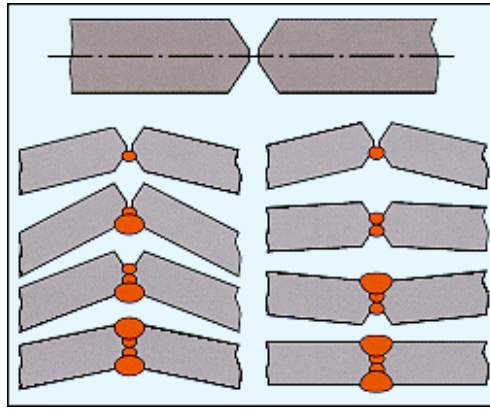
Figura 1 - Junta de topo - chanfro simétrico com múltiplos passes. (a) Sequência de soldagem realizada de forma incorreta com presença de distorção angular. (b) Solda balanceada livre de distorções (DOURADO, SOUZA, et al., 2013).
